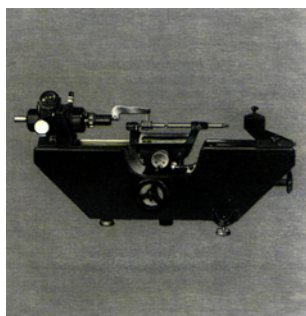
Универсальный горизонтальный длиномер с устройством для измерения шага резьбы (1959г.).
